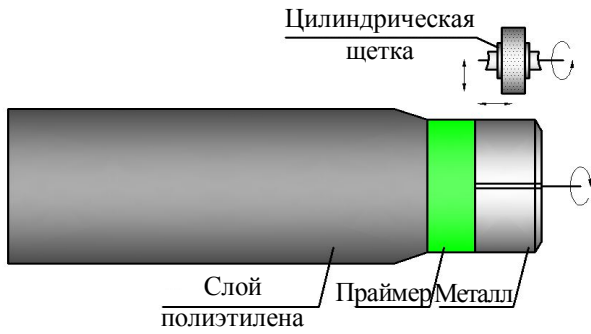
Схема обработки цилиндрической щеткой края трубы
